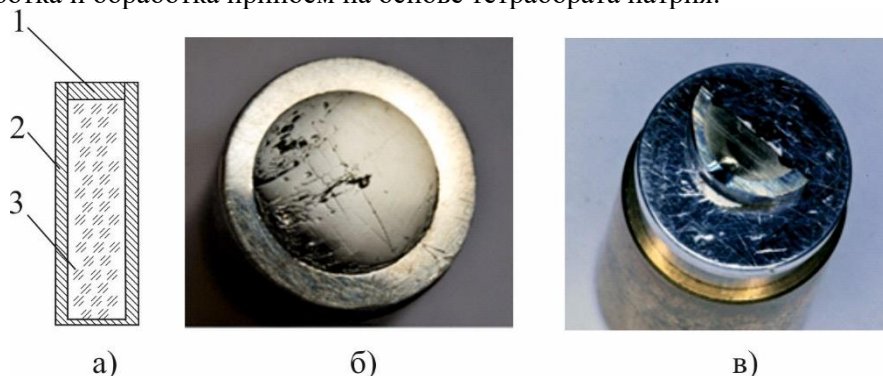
а- Схематичное изображение образца стеклометаллокомпозита (1-крышка через которую передается давление, 2-стальная заготовка, 3-стеклянный цилиндр), б- фотография среза готового образца, в- фотография микрошлифа образца
